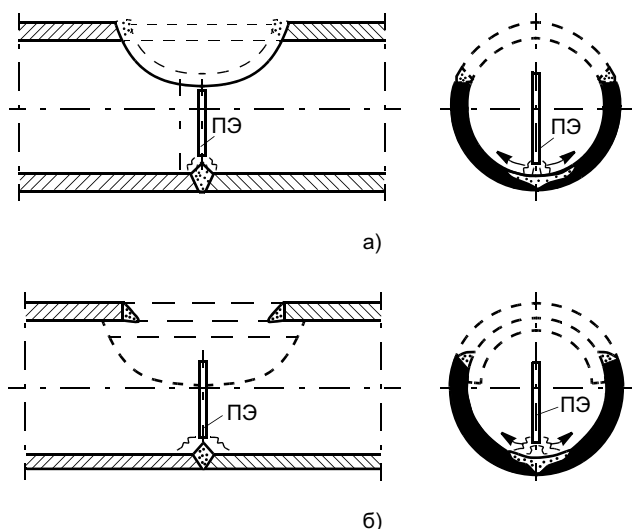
Ремонт ССС путем заварки дефектного места с внутренней поверхности кольцевого шва с последующим заглушением окна (ввод плавящего электрода (ПЭ) при сварке обеспечивается через окно на участке трубопровода): а — приварка заплаты к верхнему окну стыковым швом; б — приварка заплаты угловым швом
